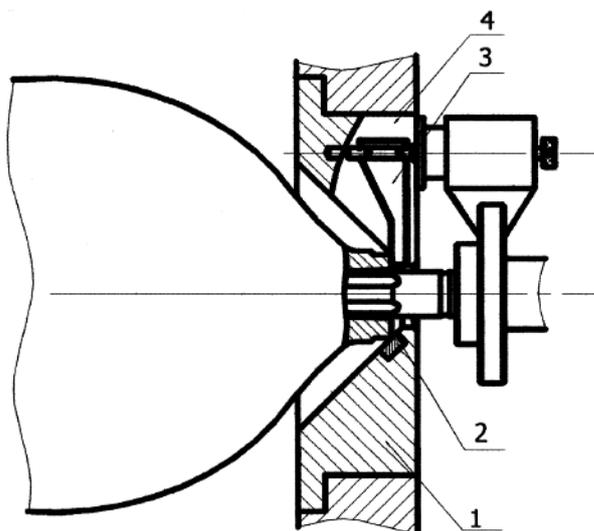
Схема наладки останова рабочего хода инструментальной головки:
